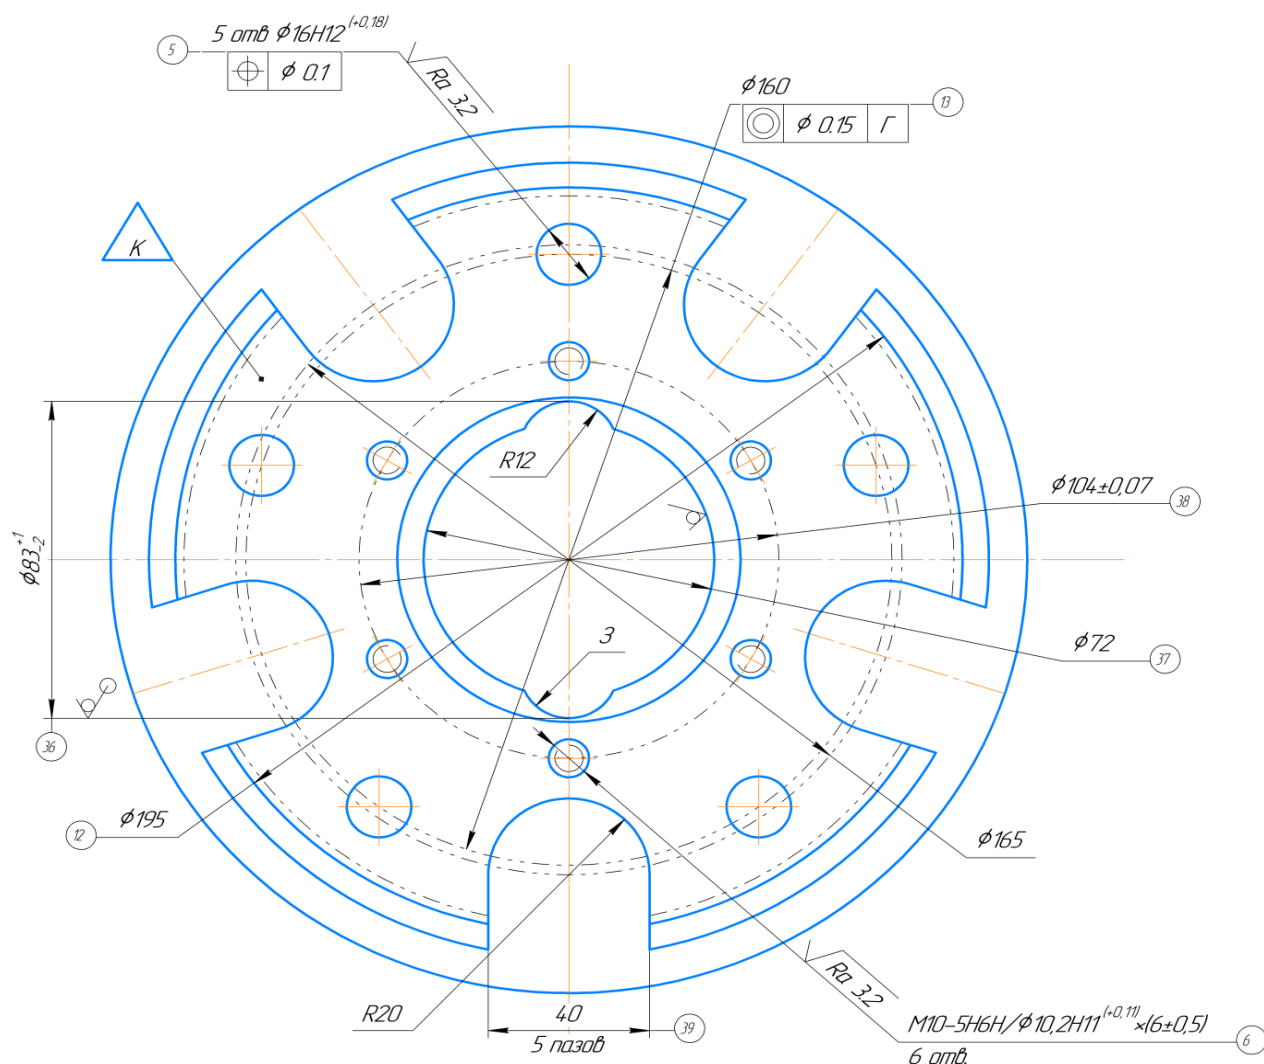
Вид Б по чертежу. Нумерация поверхностей детали.
